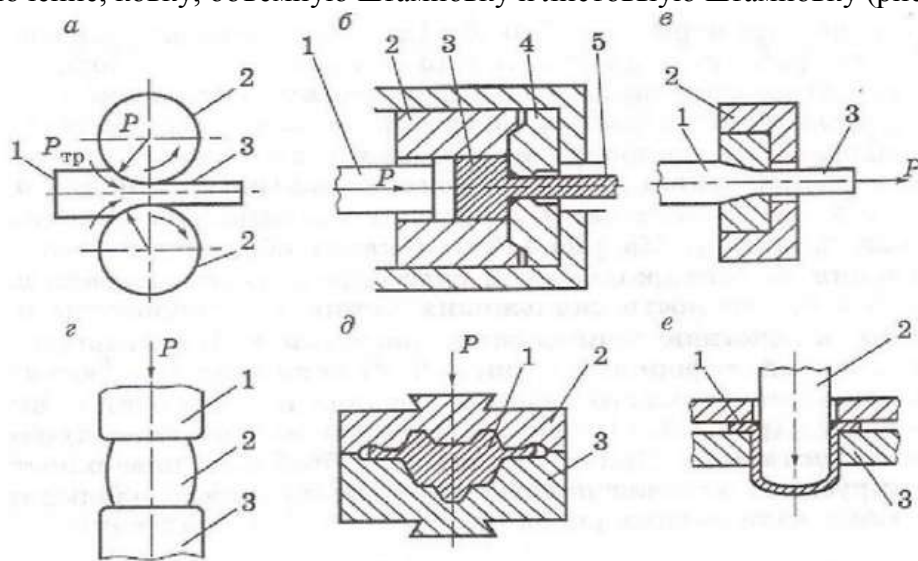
Виды обработки металлов давлением: а – прокатка (1 – заготовка, 2 – валки, 3 – изделие); б – прессование (1 – пуансон, 3 – заготовка, 5 – изделие, 2, 4 – элементы пресс-формы); в – волочение (1 – заготовка, 2 – волока, 3 – изделие); г – ковка (1, 2 – верхний и нижний бойки, 3 – заготовка); д – объемная штамповка (1 – заготовка, 2, 3 – верхняя и нижняя половины штампа); е – листовая штамповка (1 – заготовка, 2 – пуансон, 3 – матрица)
